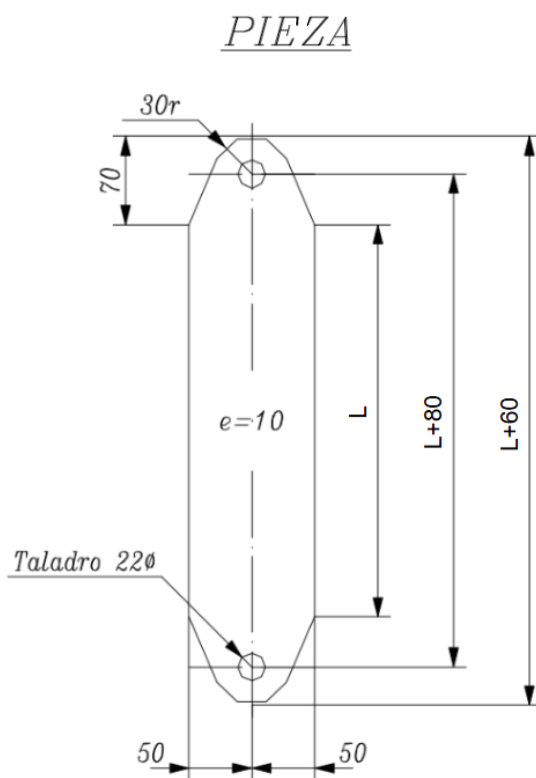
Detalle pieza de acero para sujeción de cadena de aislamiento
